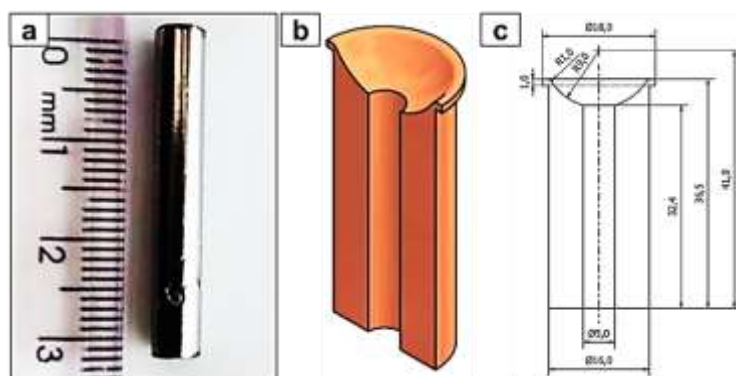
a) Cilindro obtido por sucção em molde de Cu, b) desenho do molde de Cu e c) vista esquemática de perfil com as medidas do mole.
